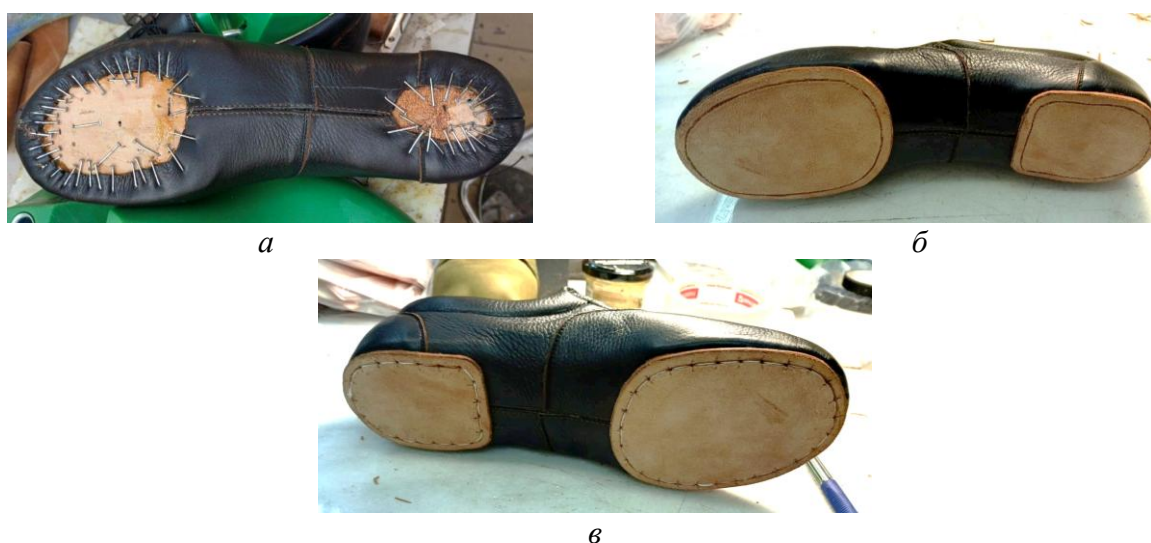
Затянутая заготовка (а), прорезанное углубление под ниточный шов (б), готовая полупара (в) (фото: асп. Бурцев А.И., рук. Карасева А.И.)
